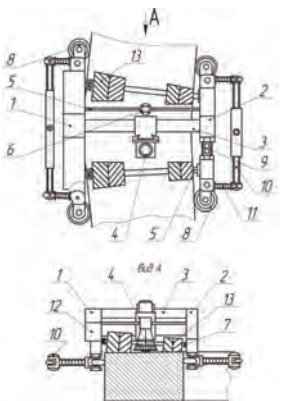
Передвижной фрезерный модуль для обработки поверхностей торцов опорных бандажей – деталей кольцевого типа
